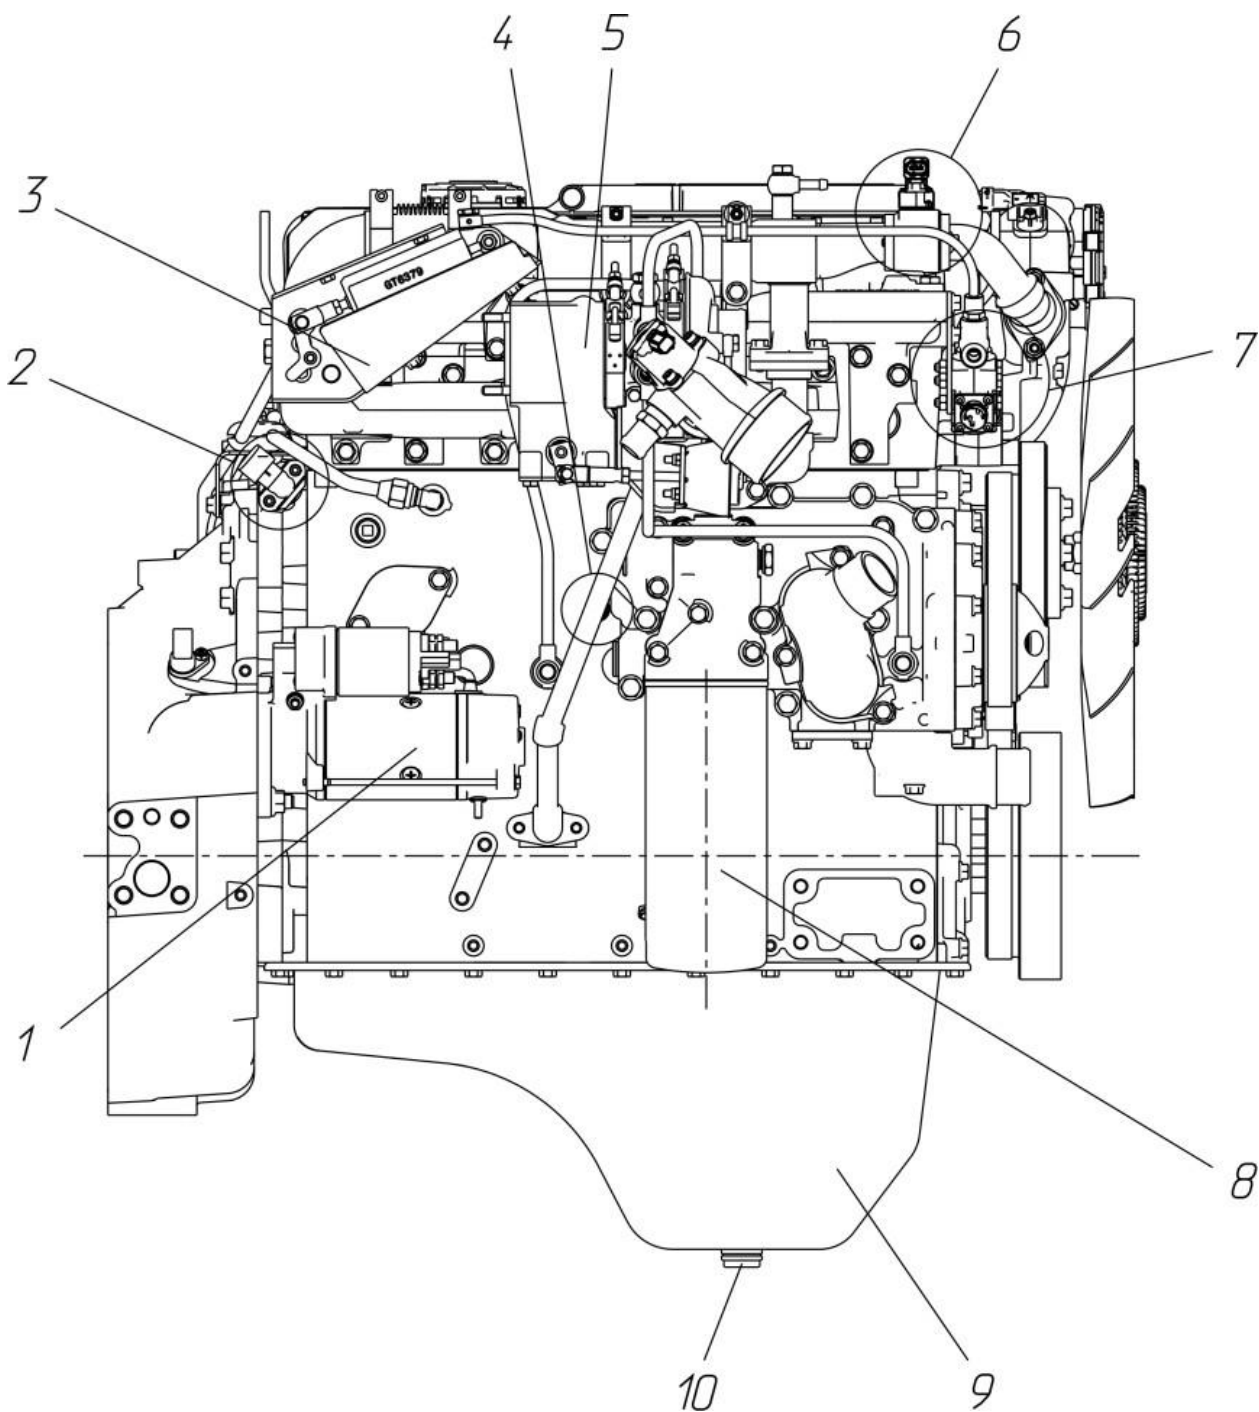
Расположение агрегатов и узлов двигателя ЯМЗ-53444-20 (вид справа):
